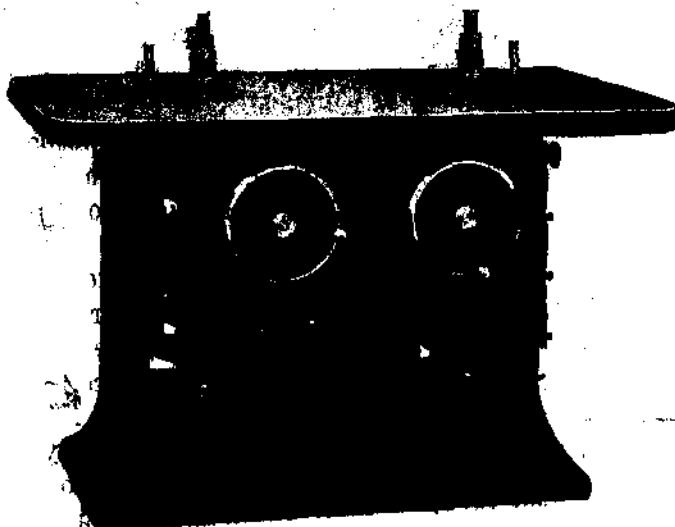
а. Фрезерный станок с двумя моторами и мешалками.
